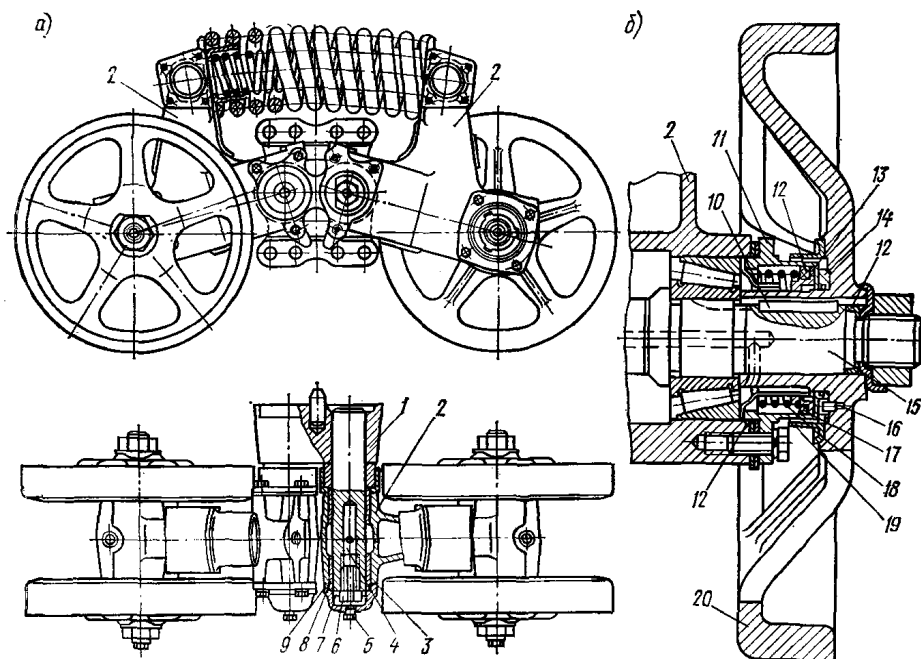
Подвеска гусеничного трактора: а – каретка; б – опорный каток
